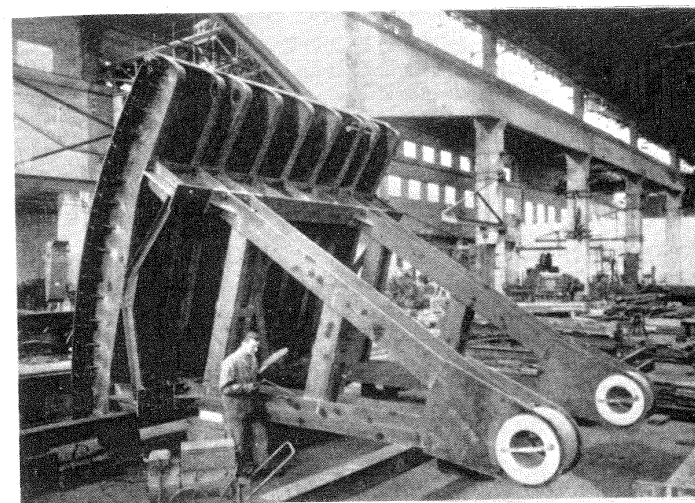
Compuerta Tainter construida por la casa Neyrpic para la central de Vaussaire, Francia.
